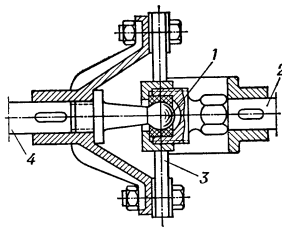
Упругий карданный механизм: 1 — центрирующий шаровой палец; 2, 4 — валы; 3 — гибкие элементы.
